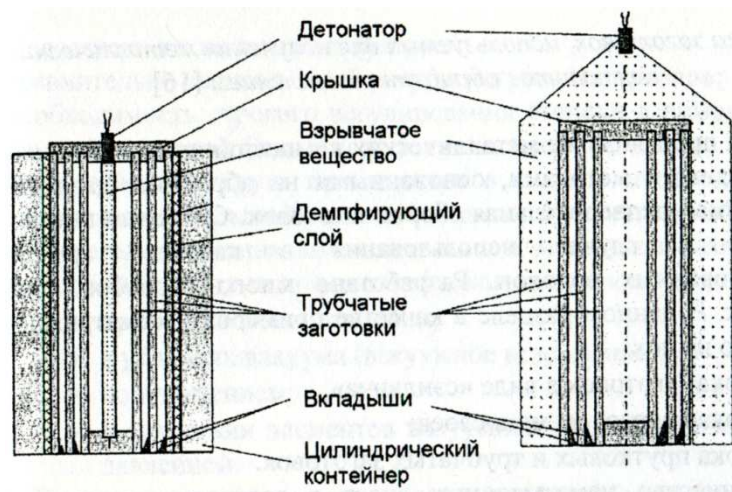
Схема сварки взрывом многослойных трубчатых заготовок
